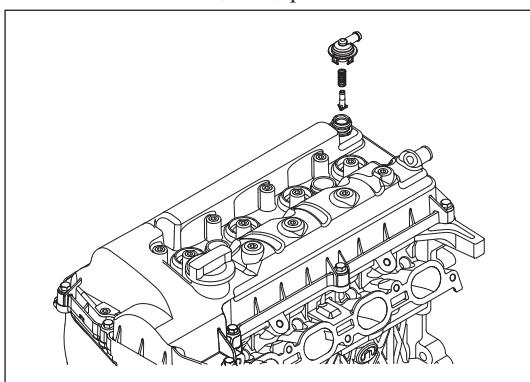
Установка системы принудительной вентиляции картера
